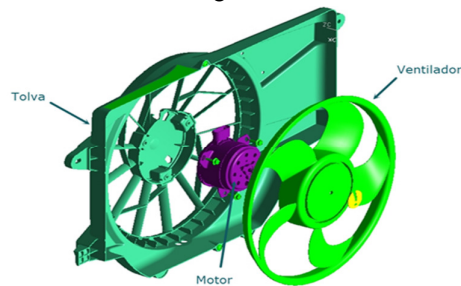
Componentes principales de un (SEA). Tomado de [20]
